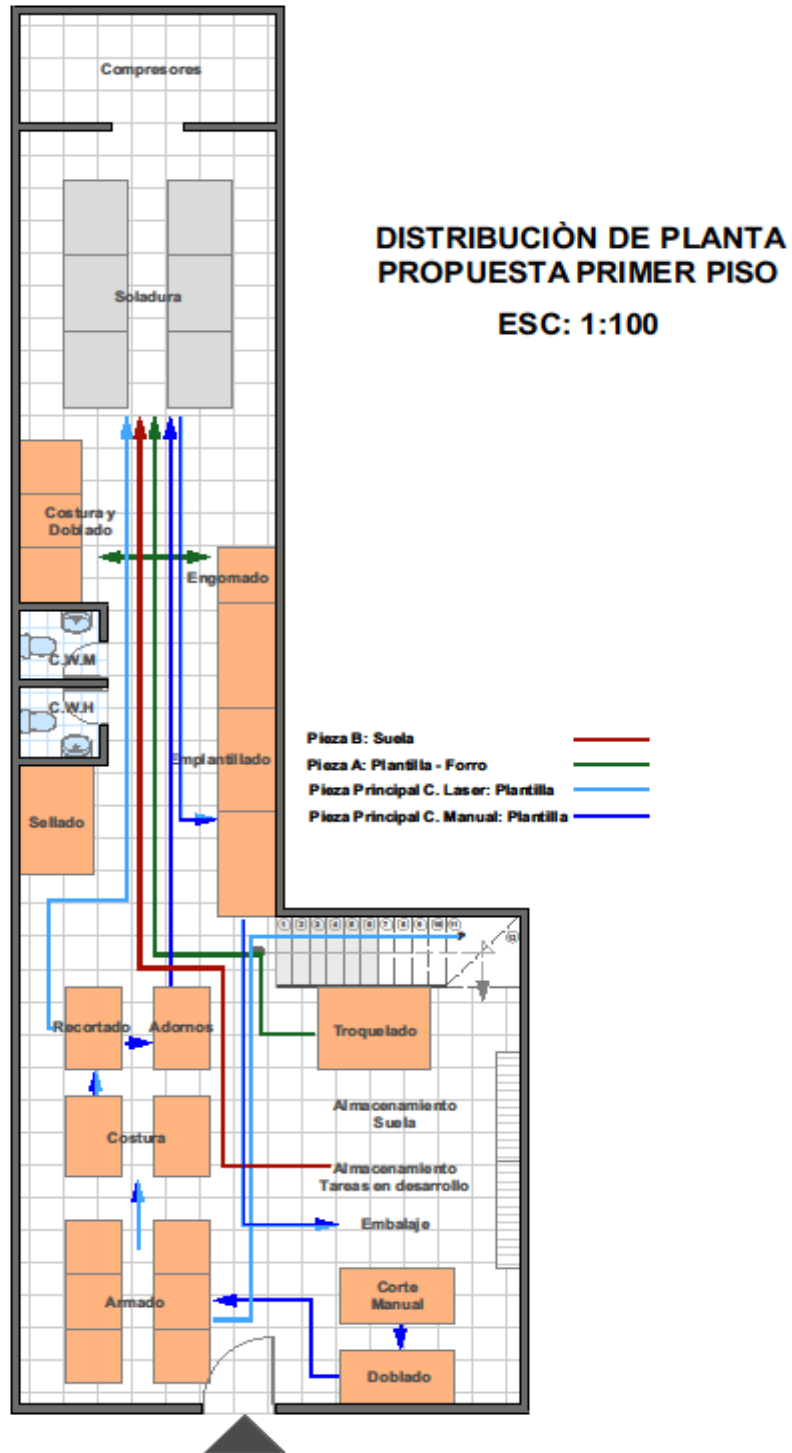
Distribución de planta propuesta primer piso calzado D'Lady y Fashion Women
